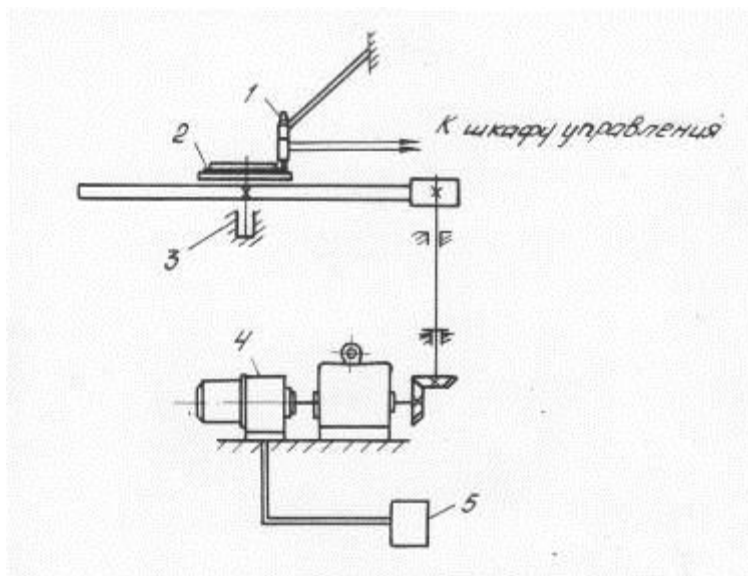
Кинематическая схема опытной установки для высокоскоростного газопламенного напыления дисковых сошников зерновых сеялок
